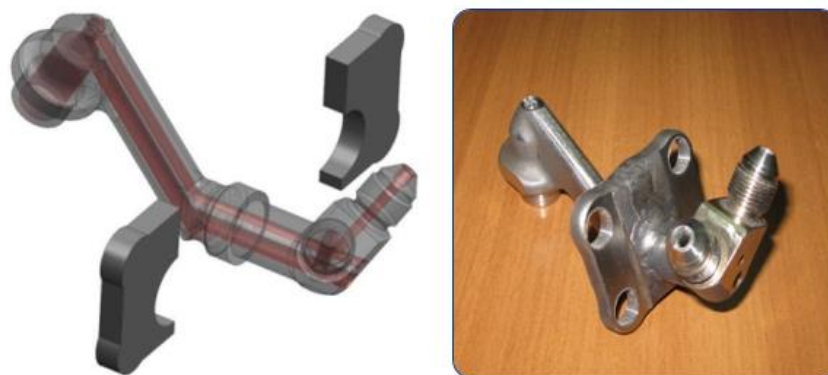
Сварная и «выращенная» топливная форсунка
